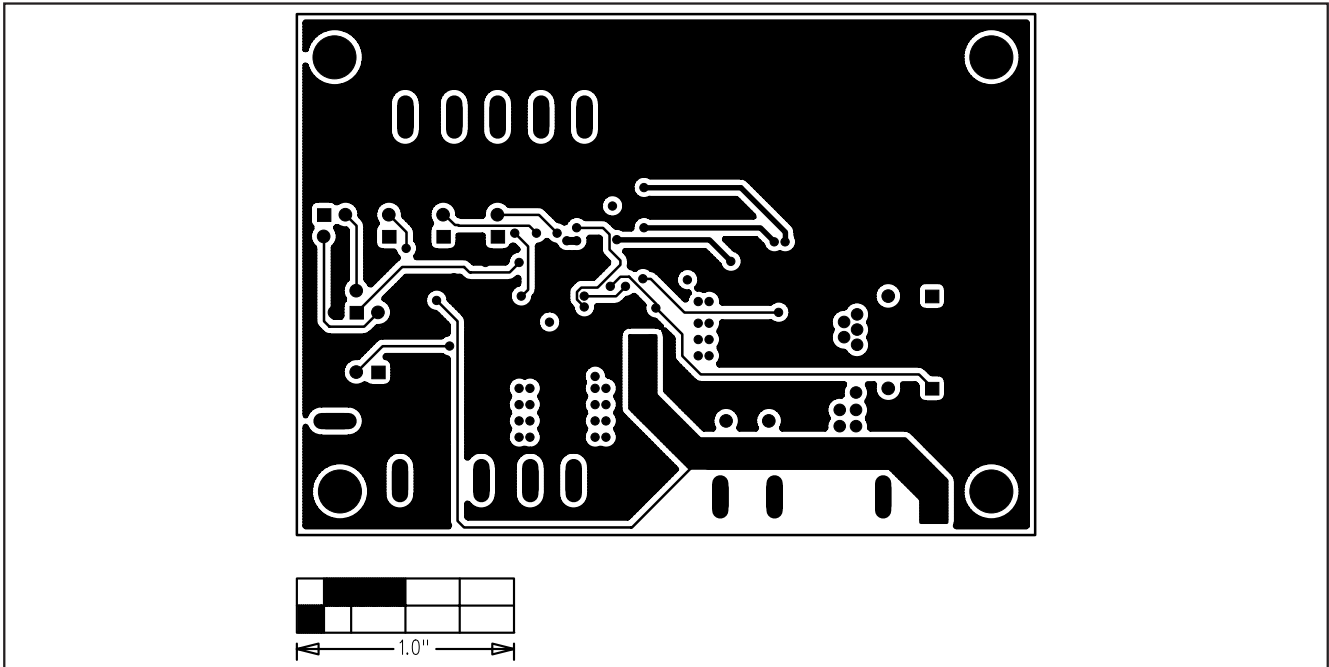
MAX8550 评估板PC 板布局 —— 焊接层
